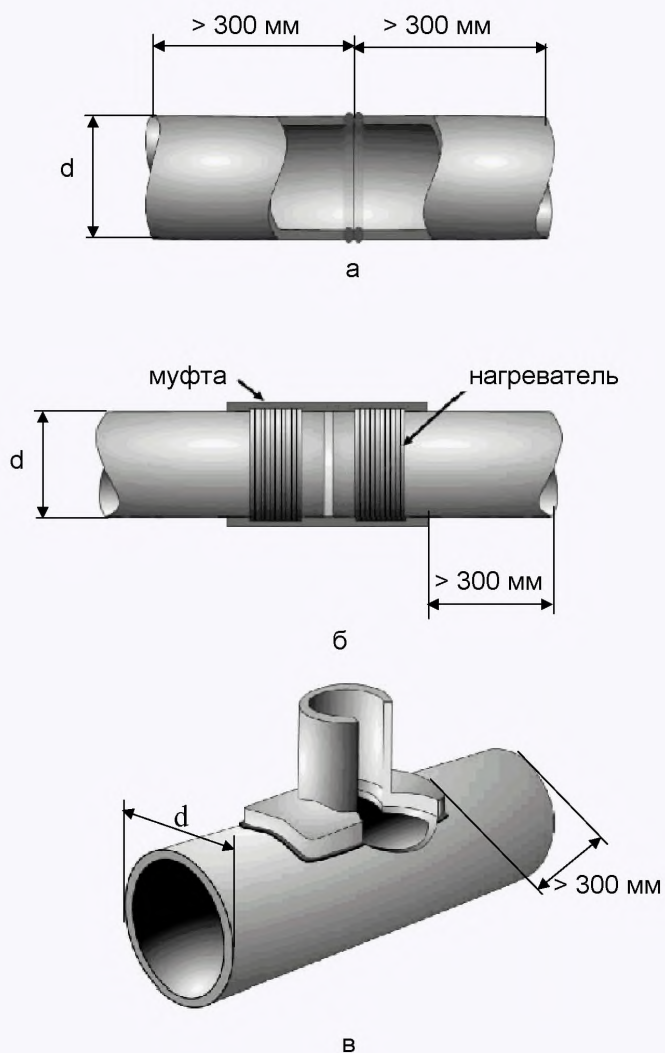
Типы контрольных сварных соединений при сварке труб из полимерных материалов:
